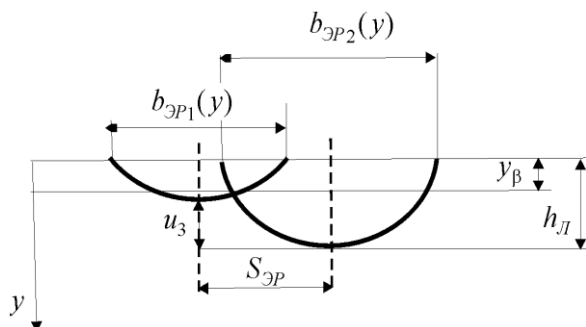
До розрахунку ймовірності видалення матеріалу заготовки ерозійними розрядами.
